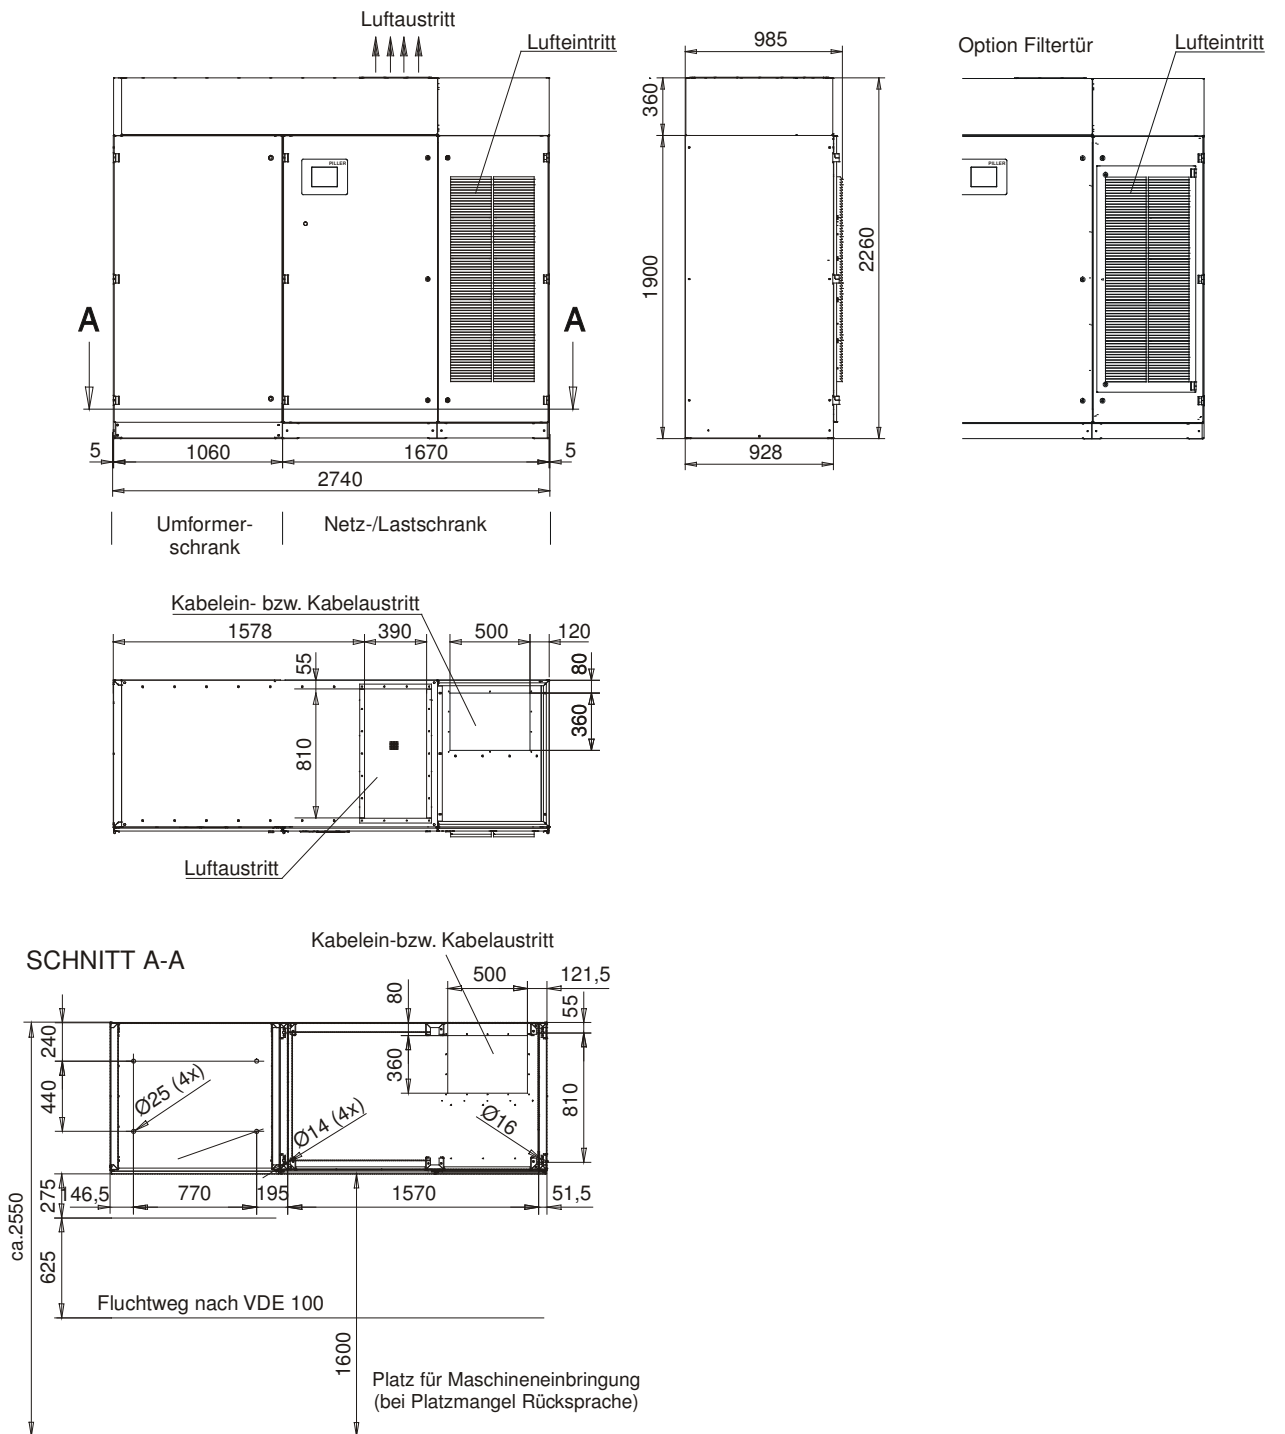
Abmessungen UB420 – UB625 mit Schalldämpfer
